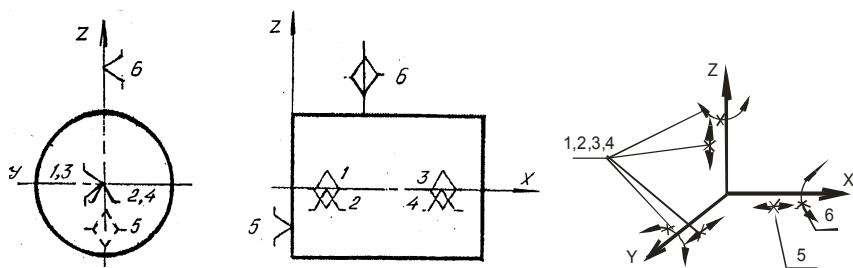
Теоретическая схема базирования заготовки типа вала по оси цилиндрической и плоской поверхностям
